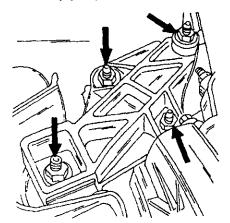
Стрелками показаны гайки крепления правой подвески двигателя. Все болты затягиваются моментом 45 нм.
